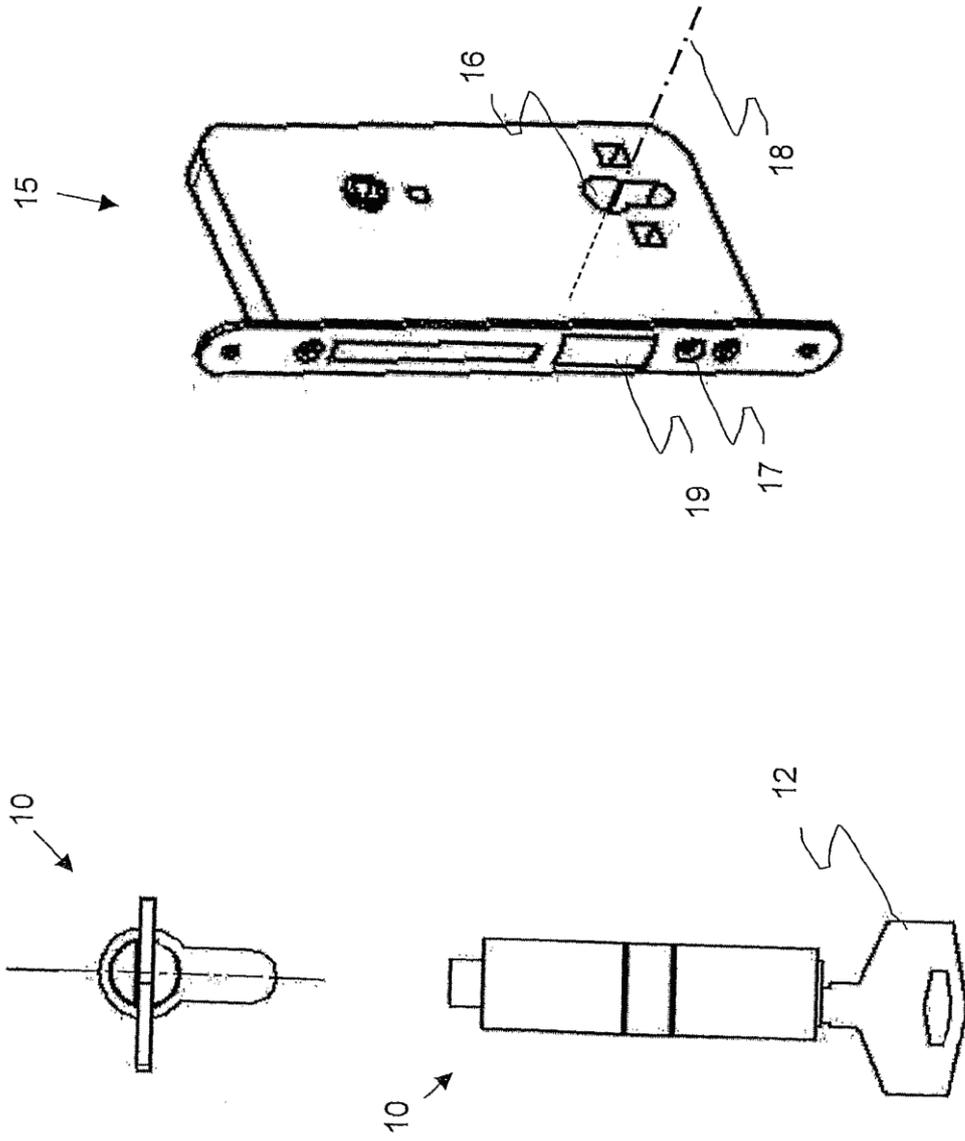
A – TÉCNICA ANTERIOR      FIG. 1B – TÉCNICA ANTERIOR
